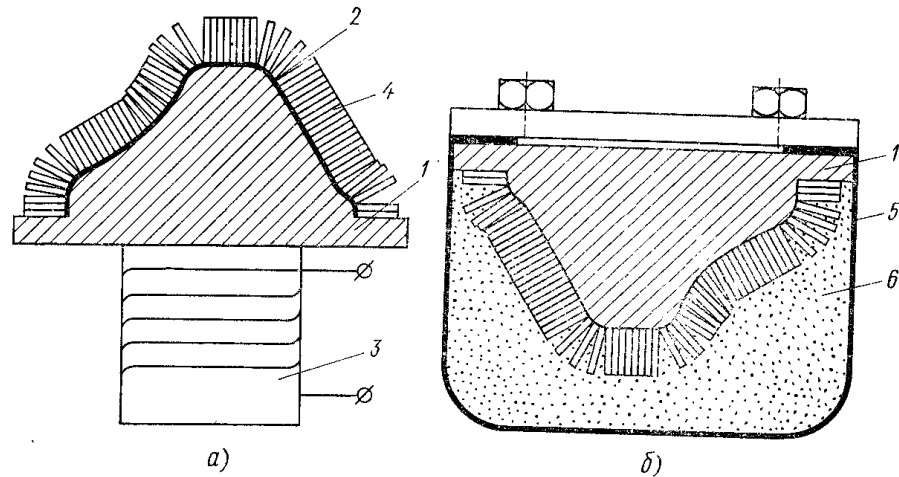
Схема виготовлення голчастих кокілів, скріплених спіканням: а – установка голок; б – підготовка до пресування
